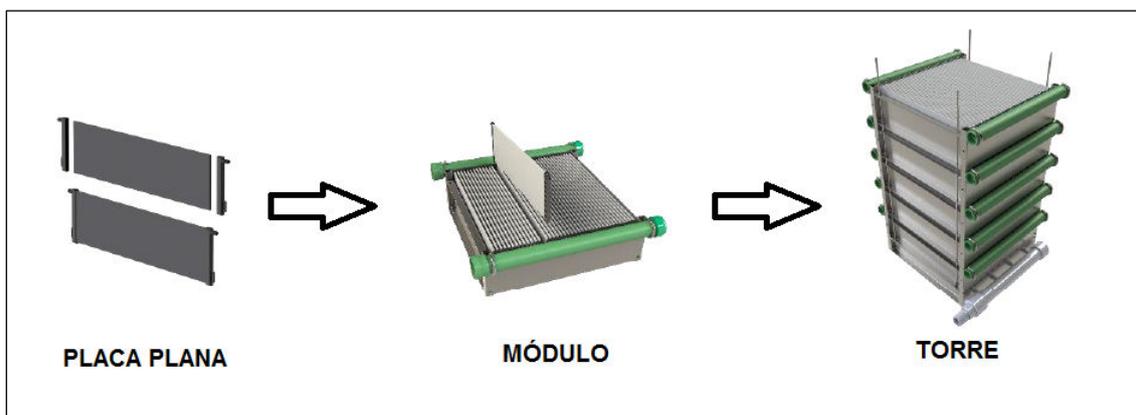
Ilustração da montagem do módulo e torre da membrana¹
